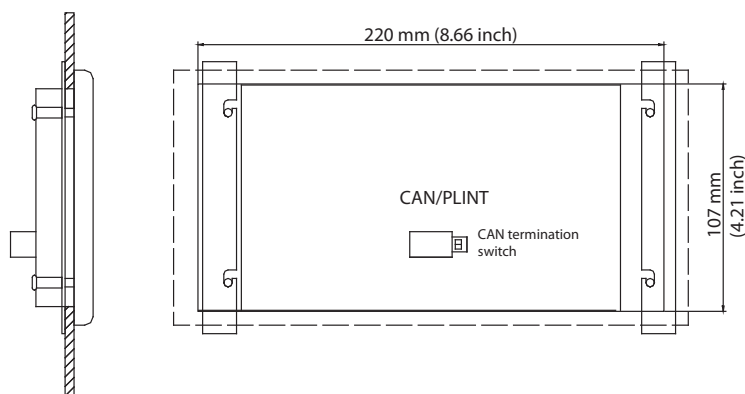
Links: Montage der Bedientafel an einer Tür. Rechts: Hinteransicht der Montage in einer Aussparung mit Abmessungen der benötigten Aussparung.
